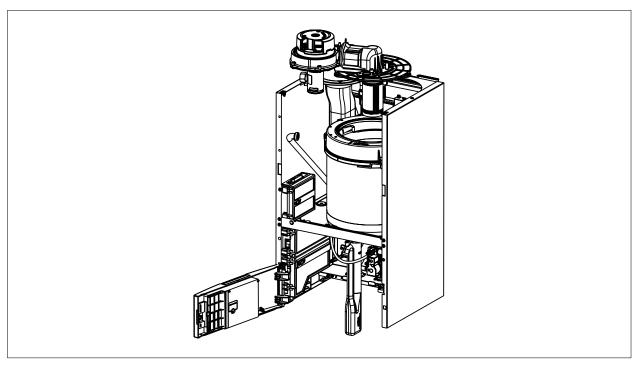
Soulever le couvercle de la chambre de combustion
